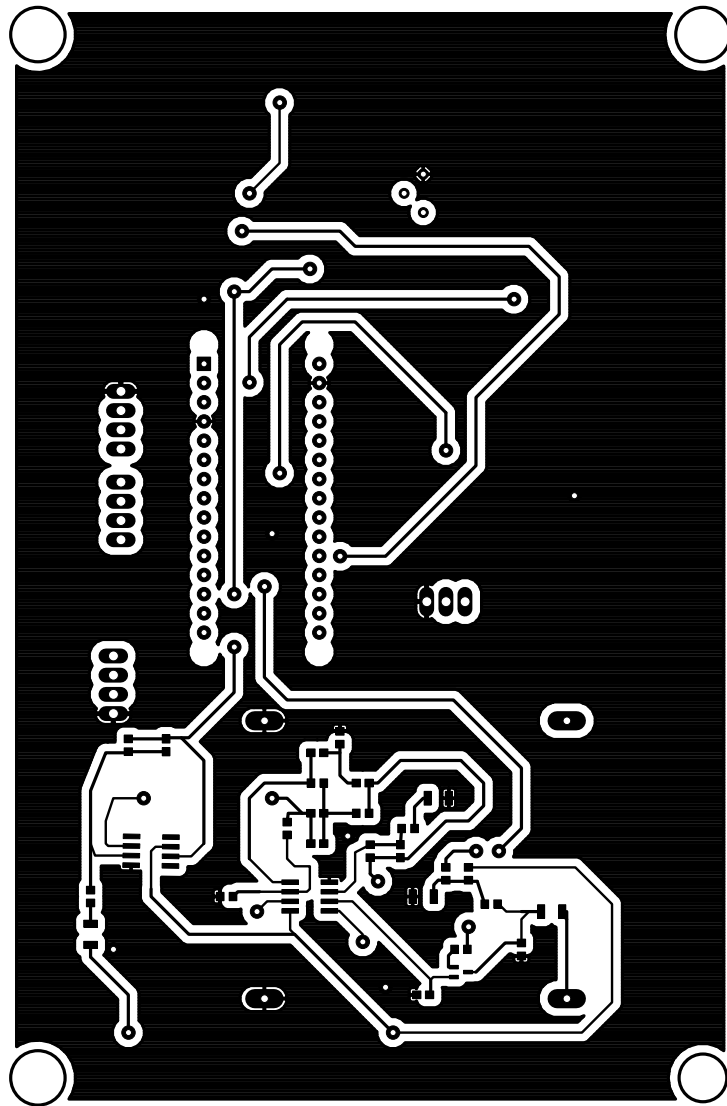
PCB para o sensor de movimento externo (Bottom).
